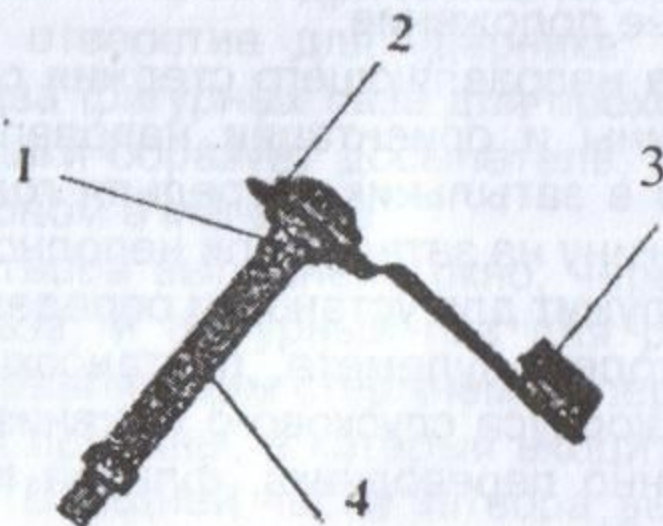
Замыкатель кожуха: 1 — выступ; 2 — шайба; 3 — флажок; 4 — собственно замыкатель
